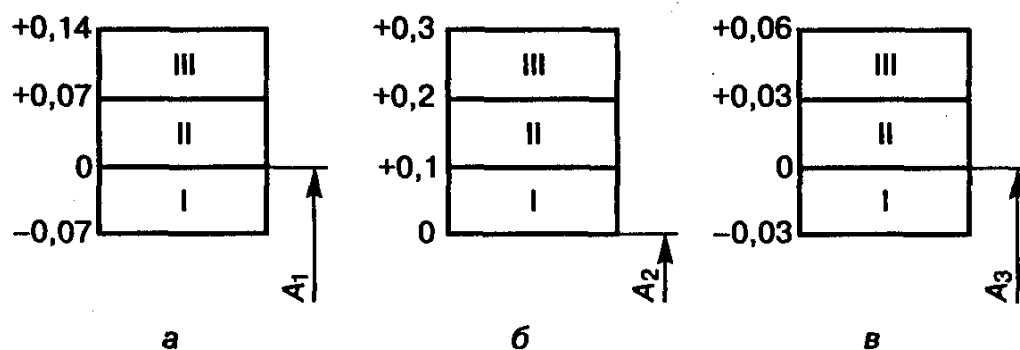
Поля допусков I, II и III групп сортировки для шестерни (а), корпуса (б) и простановочного кольца (в) сборочной единицы, изображенной на рис. 1.3
